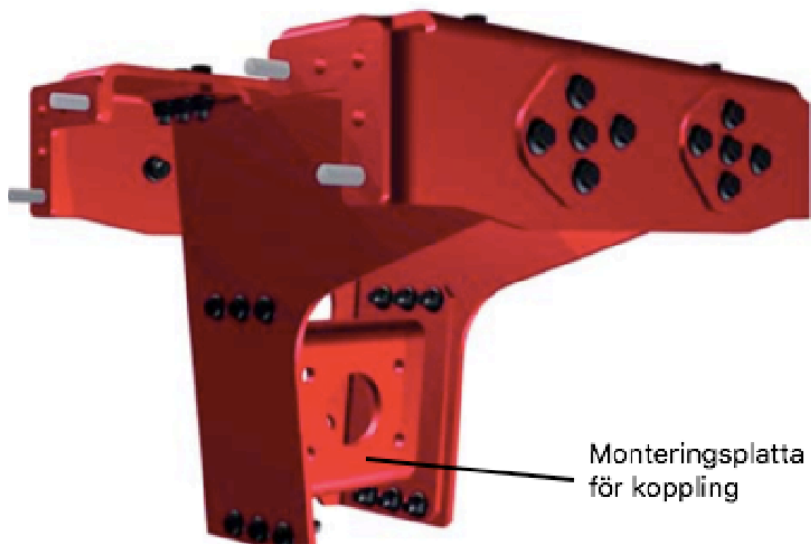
Dragbalk utan koppling anpassad för underliggande montage
